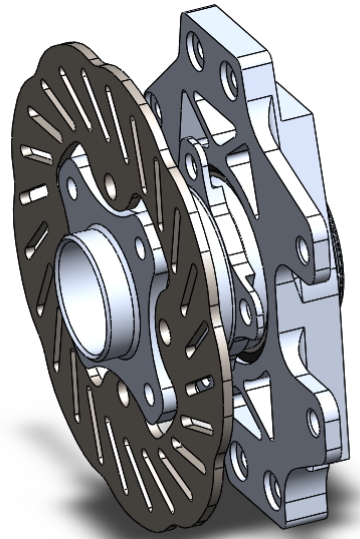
Detalhe para a livre passagem do disco de freio pela flange de fixação da roda.
